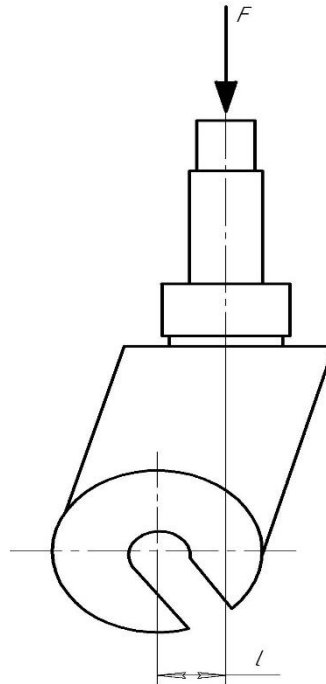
Схема розрахунку вилки поворотного колеса
